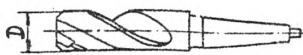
зенкер, оснащенный пластинками из твердого сплава
